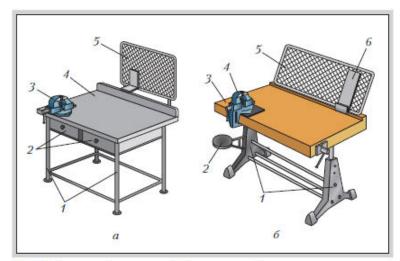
Верстаки: a — слесарный: 1 — основание; 2 — ящики для инструментов; 3 – тиски; 4 – крышка; 5 – защитная сетка; 6 – универсальный: 1 — основание; 2 — сиденье; 3 — крышка; 4 — тиски; 5 — защитная сетка; 6 — подставка для технической документации
